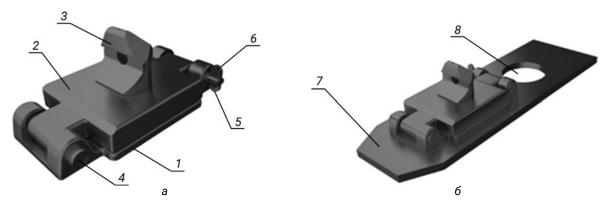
Устройство для крепления контейнеров на платформе (патент RU 2687371C1) [19]: а — внешний вид; б — с установкой на нижней плите; 1 — упорная плита; 2 — плита-основание; 3 — фитинговый упор; 4 — поворотная ось; 5 — фиксирующая ось; 6 — флажок-предохранитель; 7 — нижняя плита; 8 — сквозное отверстие для размещения фитингового упора вершиной вниз
